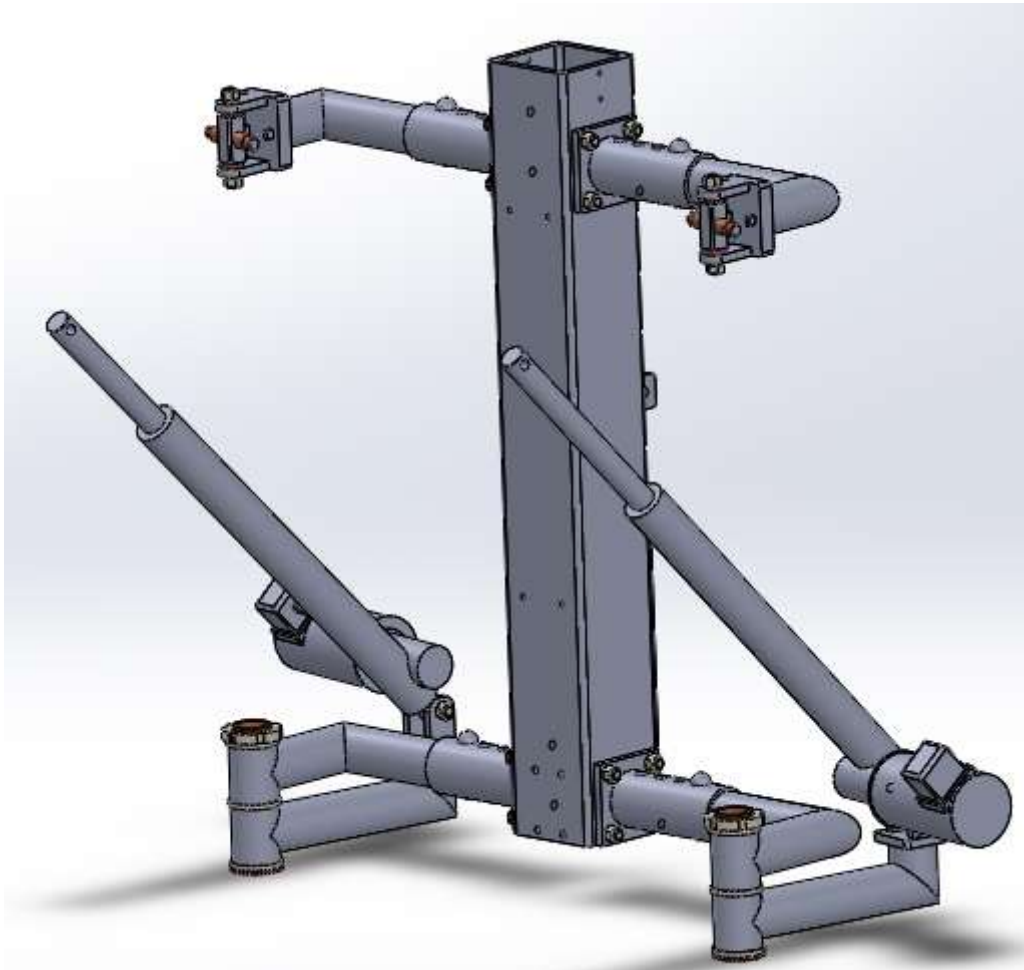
Estructuras del hombro y soporte con actuador y perfil columnar.
